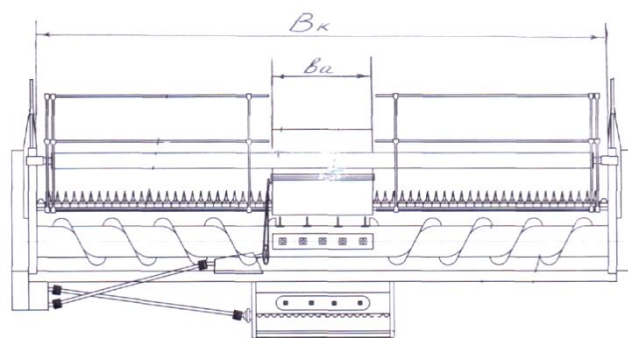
Конструктивно-технологической схема жатки с очесывающей приставкой
